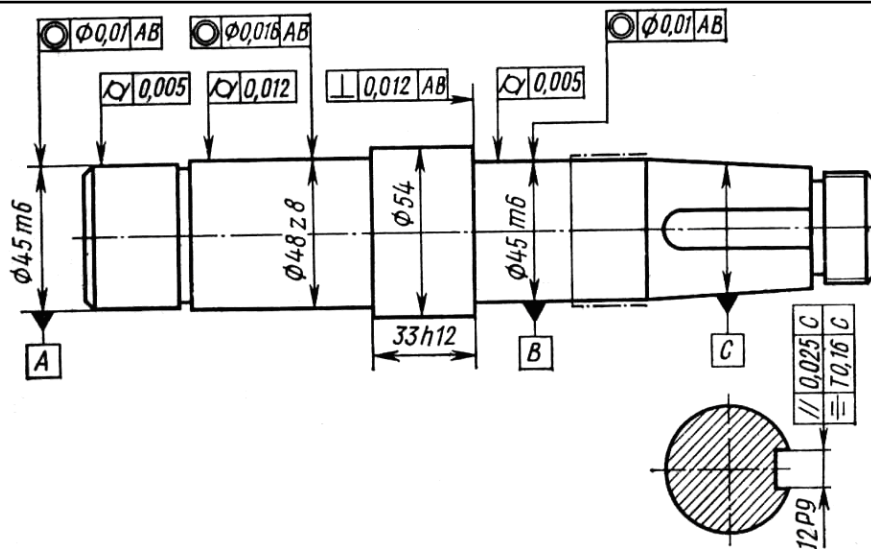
Допуски форми і розташування поверхонь вала
